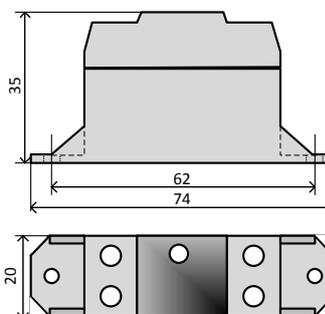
Габаритные размеры устройства для монтажа на поверхность
